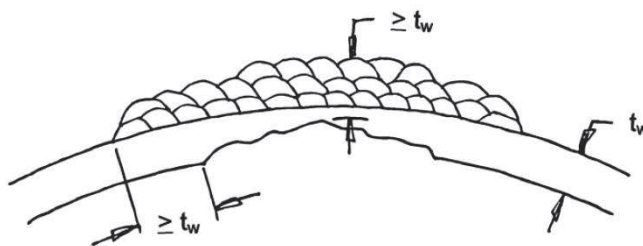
Depósito de material (soldadura), en un defecto de corrosión interna ^[5].
